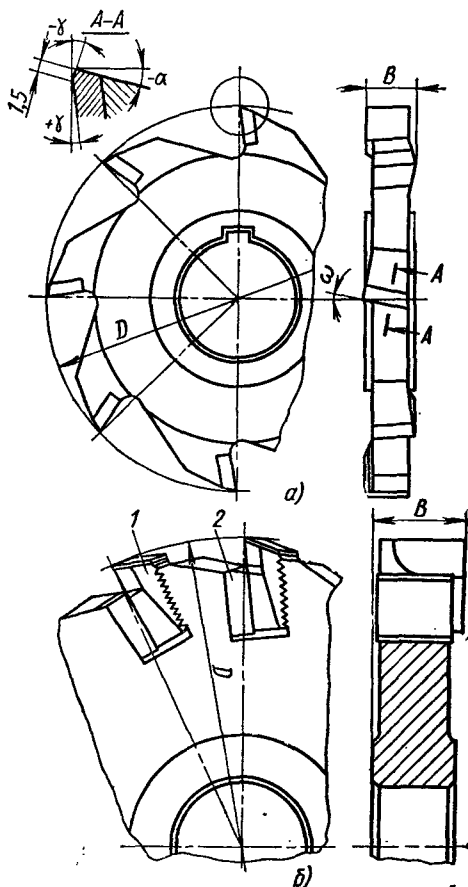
Дисковая трехсторонняя фреза: а — с папаянными пластинками из твердого сплава; б — с ножами, оснащенными твердосплавными пластинками
